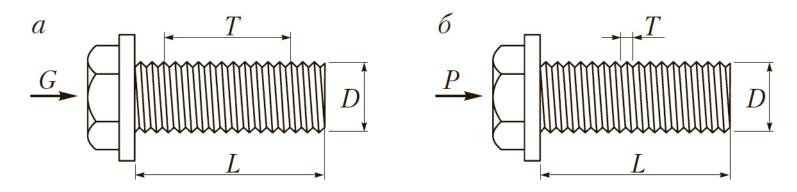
Размеры/маркировка класса прочности болтов: a — маркировка SAE: G — маркировка класса прочности; L — длина, дюймов; T — шаг резьбы, количество витков на дюйм; D — номинальный диаметр, дюймов;  $\delta$  — метрическая маркировка: P — класс прочности; L — длина, мм; T — шаг резьбы (расстояние между соседними витками), мм; D — номинальный диаметр, мм
